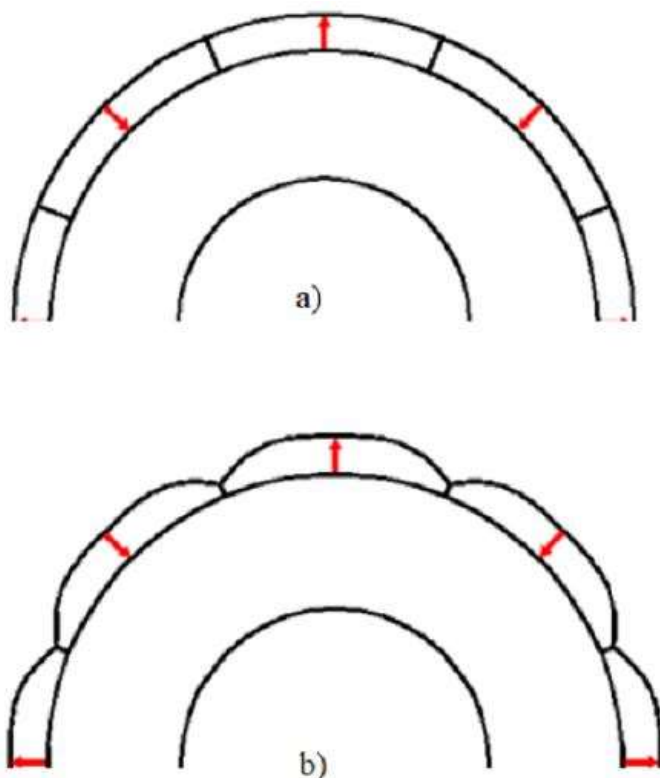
Klasický a bi-harmonický rotor IPM motoru [6]
